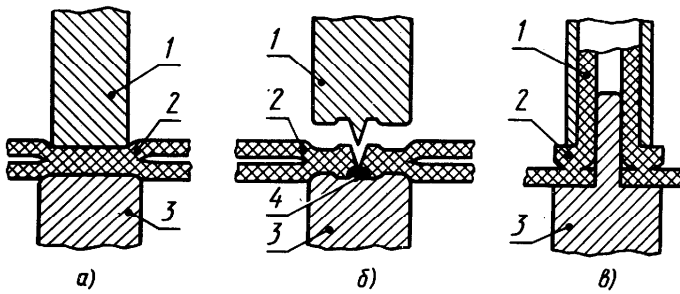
Электроды для получения сварных швов ПВХ: а - плоского; б - фигурного с разрезанием материала; в - кольцевого
